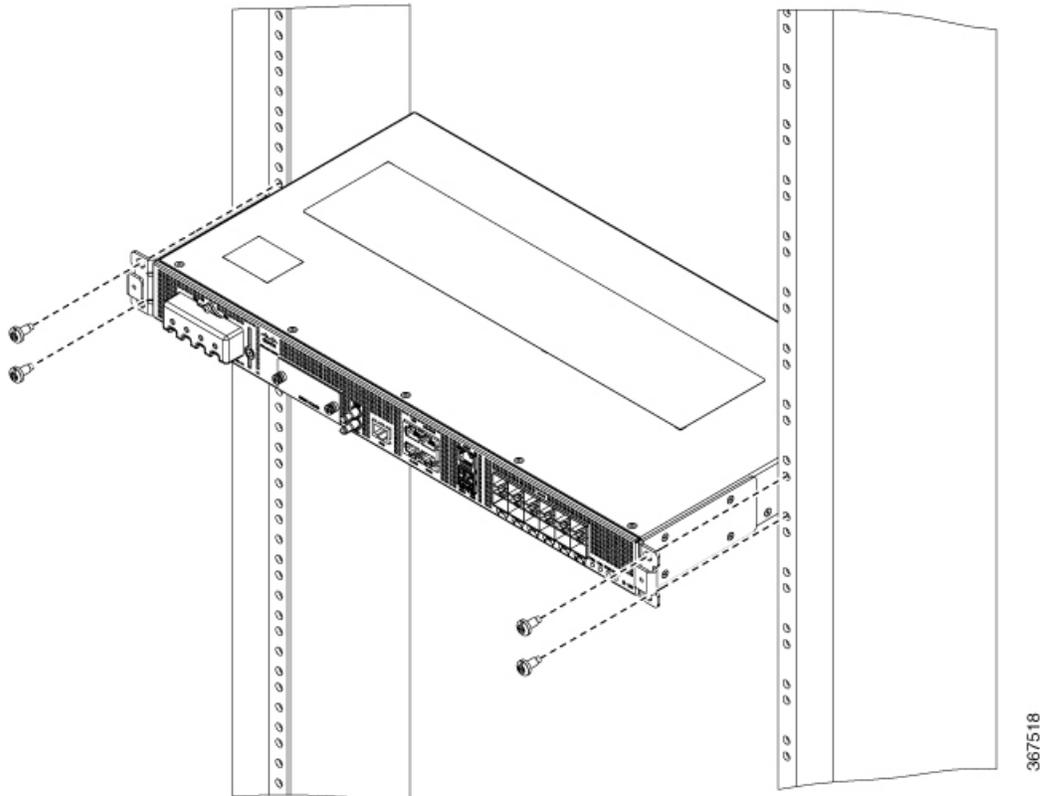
Installer l'appareil sur un rack de 19 pouces (montage central)
